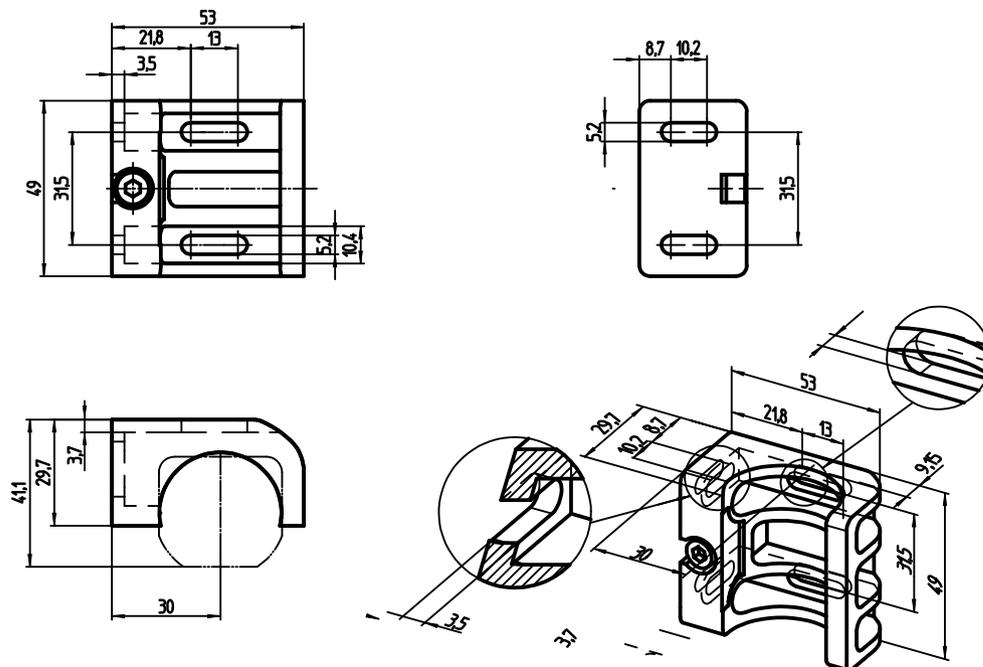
Габаритный чертеж крепления FlexFix (2066614)
